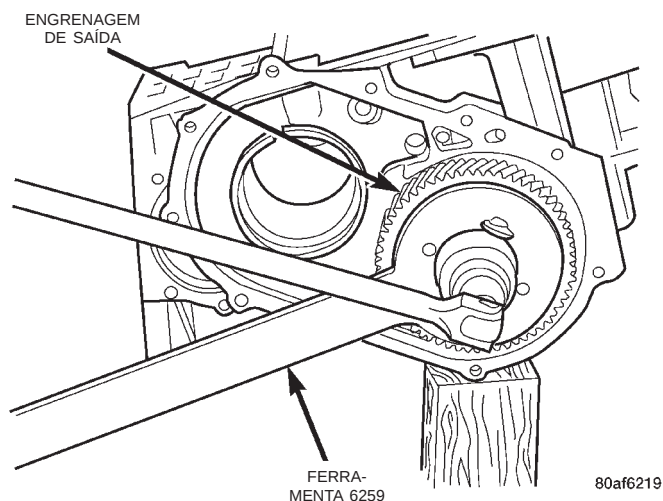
Remoção do Parafuso da Engrenagem de Saída
